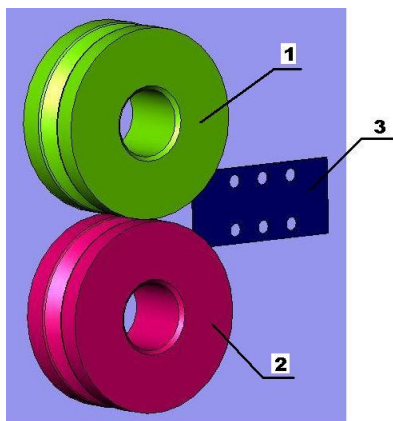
Роликовый калибр для изготовления профиля уголкового типа: 1 – верхний ролик; 2 – нижний ролик; 3 – заготовка
